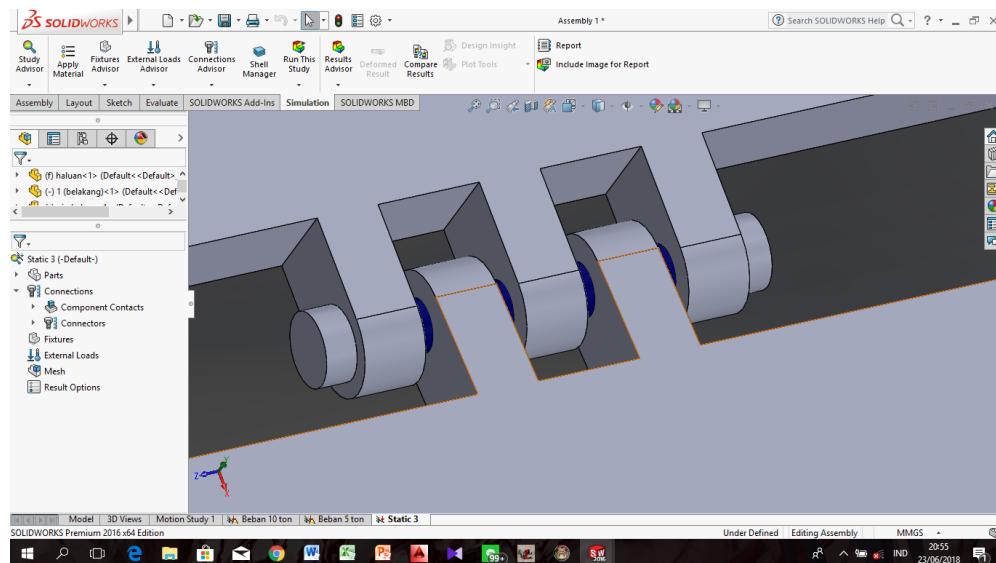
Model Solidworks ramp door pada bagian depan.
